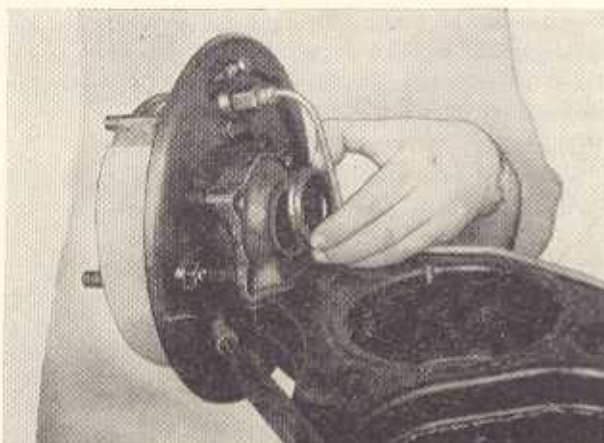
Lagerflanschöffnung mit Gummistopfen verschließen
